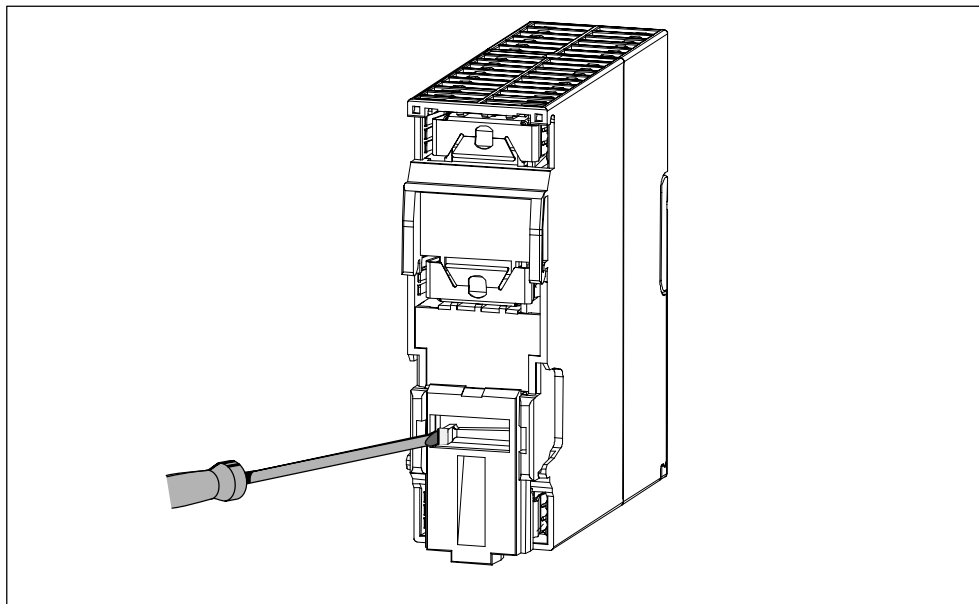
Entfernen des Schiebers zur Montage auf Profilschiene für S7-Aufbautechnik
